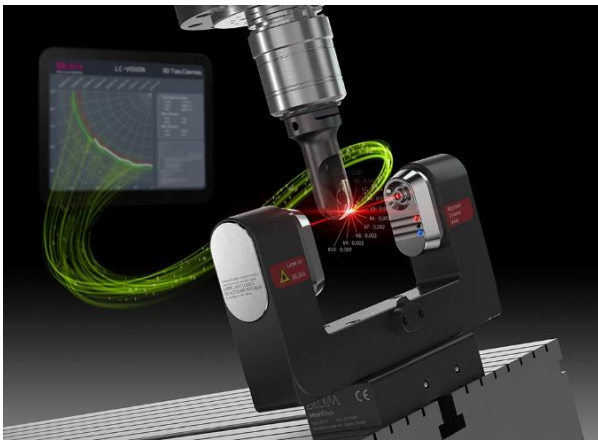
Tausende Messwerte pro Sekunde: BLUM präsentiert auf der EMO neueste Anwendungen rund um die digiloge Werkzeug- und Werkstückmessung in Werkzeugmaschinen.
